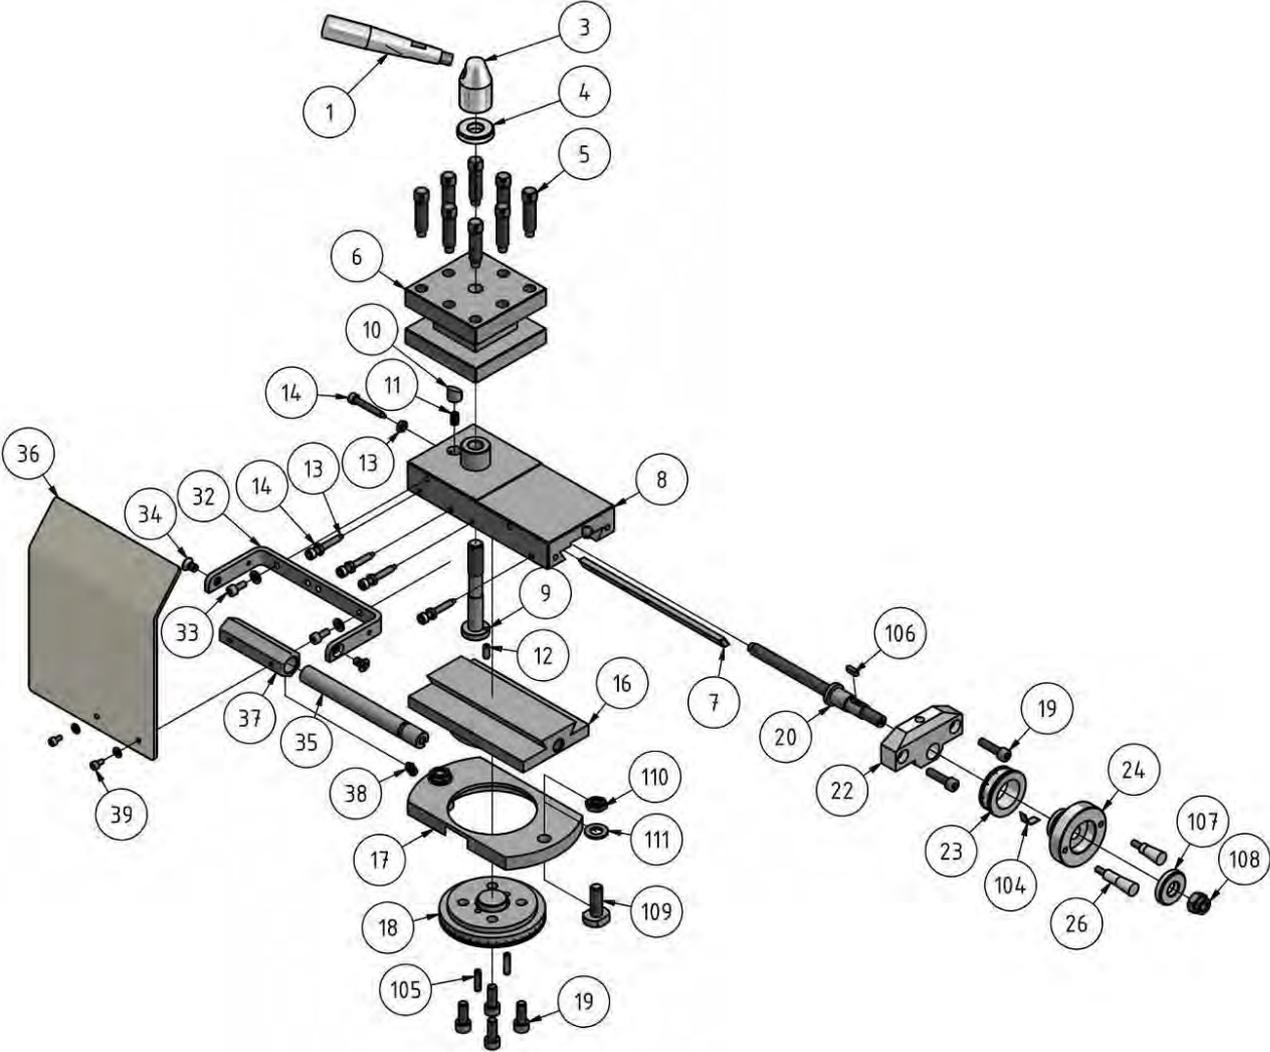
Oberschlitten - Carro superior TU 2506
